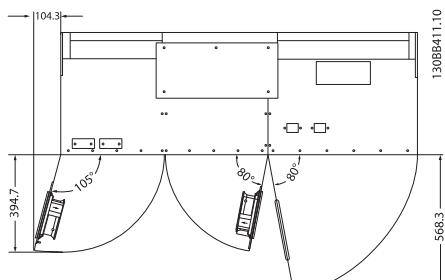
Пространство перед корпусом IP21/IP54, размер корпуса E7.
